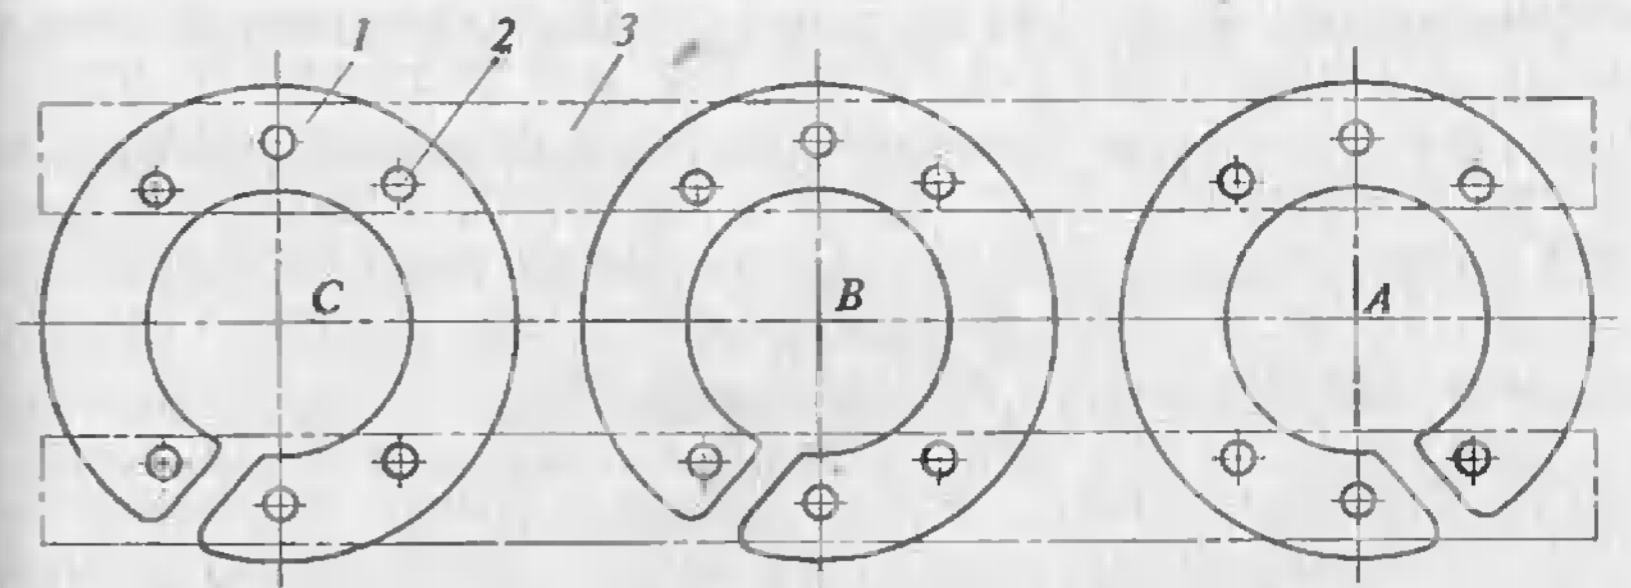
Расположение прессующих колец в трехфазном трансформаторе при общей прессовке:
